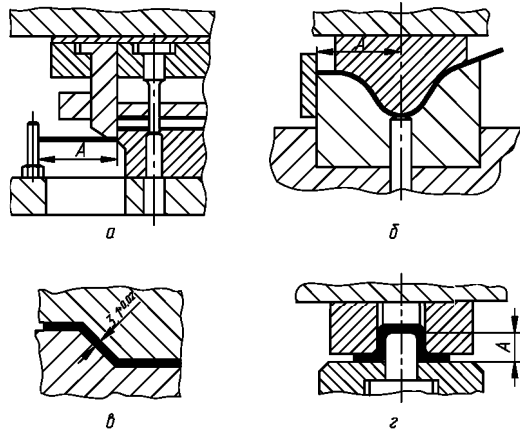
Примеры простановки спецразмеров, проверяемых при сборке штампов: а — разделительный штамп; б, в, г — формообразующие
